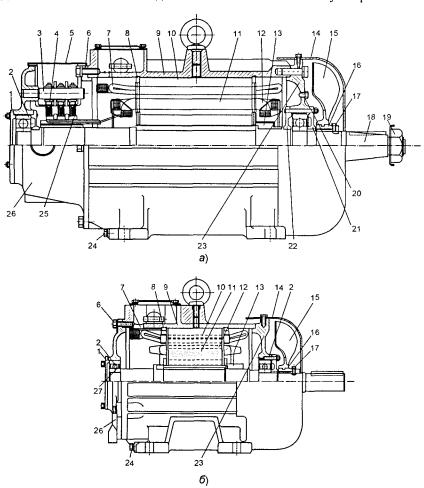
Крановые асинхронные электродвигатели: a - MT 41 с фазным ротором, 6 - MTК-11 с короткозамкнутым ротором; 1, 21 и 22 — крышки подшипниковых камер; 2 — подшипник; 3 — палец щеткодержателя; 4 — шеткодержатель; 5 — крышка окна в подшипниковом щите; 6 — болт крепления подшипникового щита; 7 — двухслойная обмотка статора; 8 — запорное кольцо сердечника; 9 — корпус статора; 10 — сердечник статора; 11 — сердечник ротора; 12 — обмотка ротора; 13 — втулка на валу, прижимающая сердечник ротора; 14 — кожух вентилятора; 15 — литой алюминиевый вентилятор; 16 — стальная втулка залитая в вентилятор; 17 — стопорный винт крепления вентилятора; 18 — конический рабочий конец вала со шпонкой; 19 — затяжная гайка; 20 — болт, закрывающий отверстие в подшипниковом щите для измерения воздушного зазора между статором и ротором; 23 и 26 — подшипниковые щиты; 24 — болт для присоединения заземления; 25 — контактные кольца; 27 — защитная шайба шарикоподшипников
